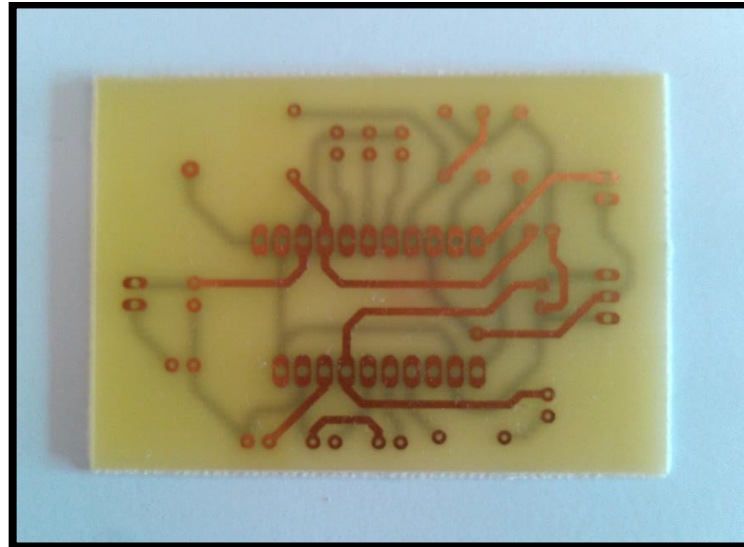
PCB del circuito del chip bq51050B sin montar (TOP)
